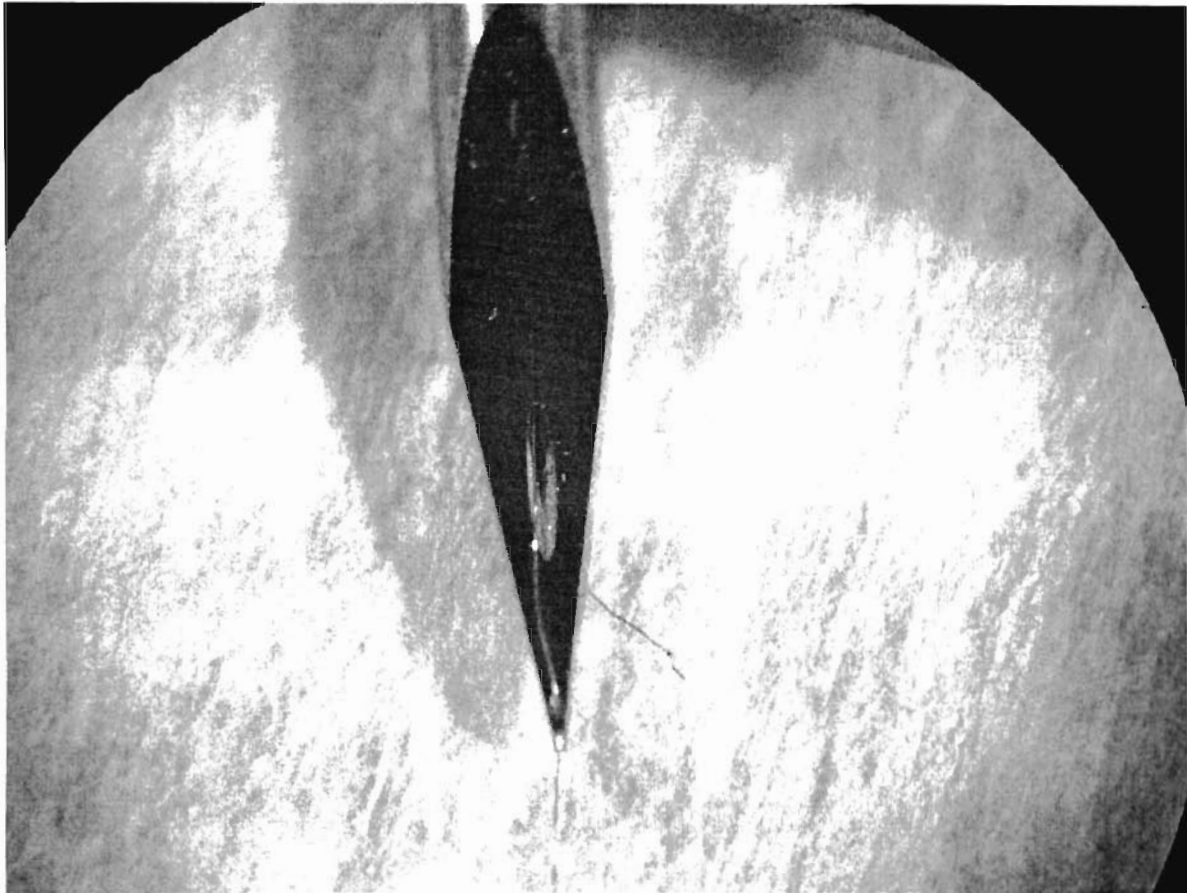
Herramienta para soldar por el método de "Wire wedge bond" (soldado de alambre con cuña) termosónico por medio de un sistema Hybond modelo 572A. IICO-UASLP.
